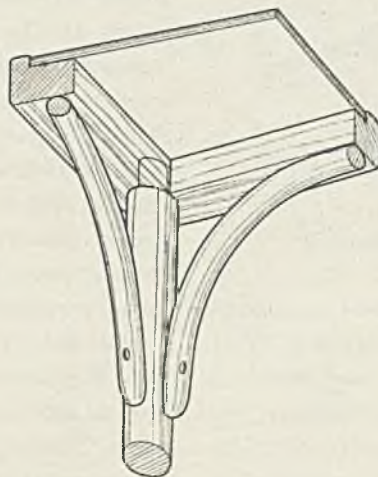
Eingeschraubte Bogen, haltbarste Verbindung
